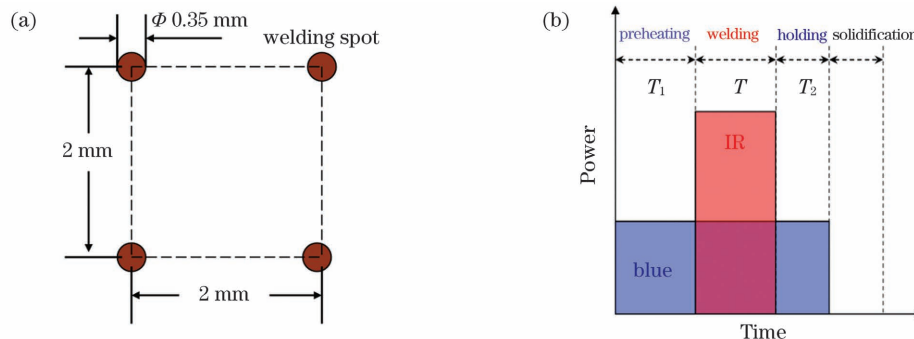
焊点的排布情况与焊接周期。(a) 拉力测试的四焊点排布;(b) 单焊点焊接时双波长激光的工作时序
